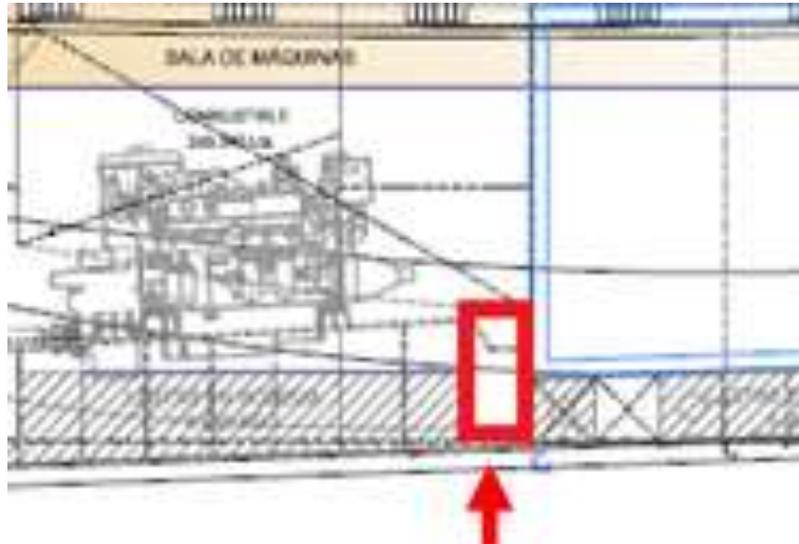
Vista perfil longitudinal – Ubicación de la toma de mar sobre la banda de estribor
